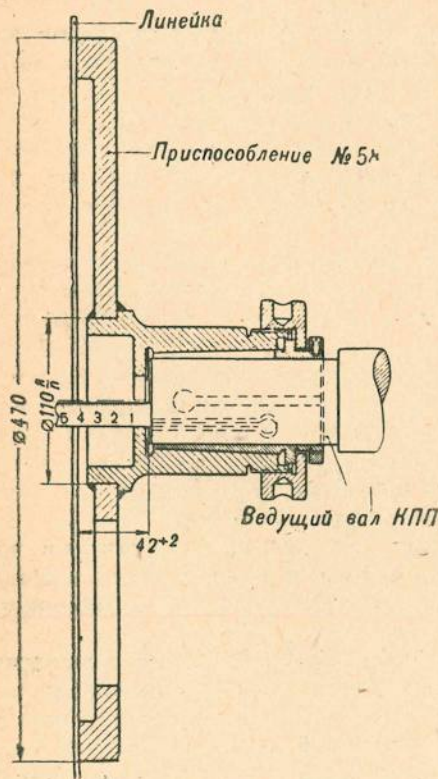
Проверка размера от торца ведущего вала коробки перемены передач до торца диска приспособления № 58
